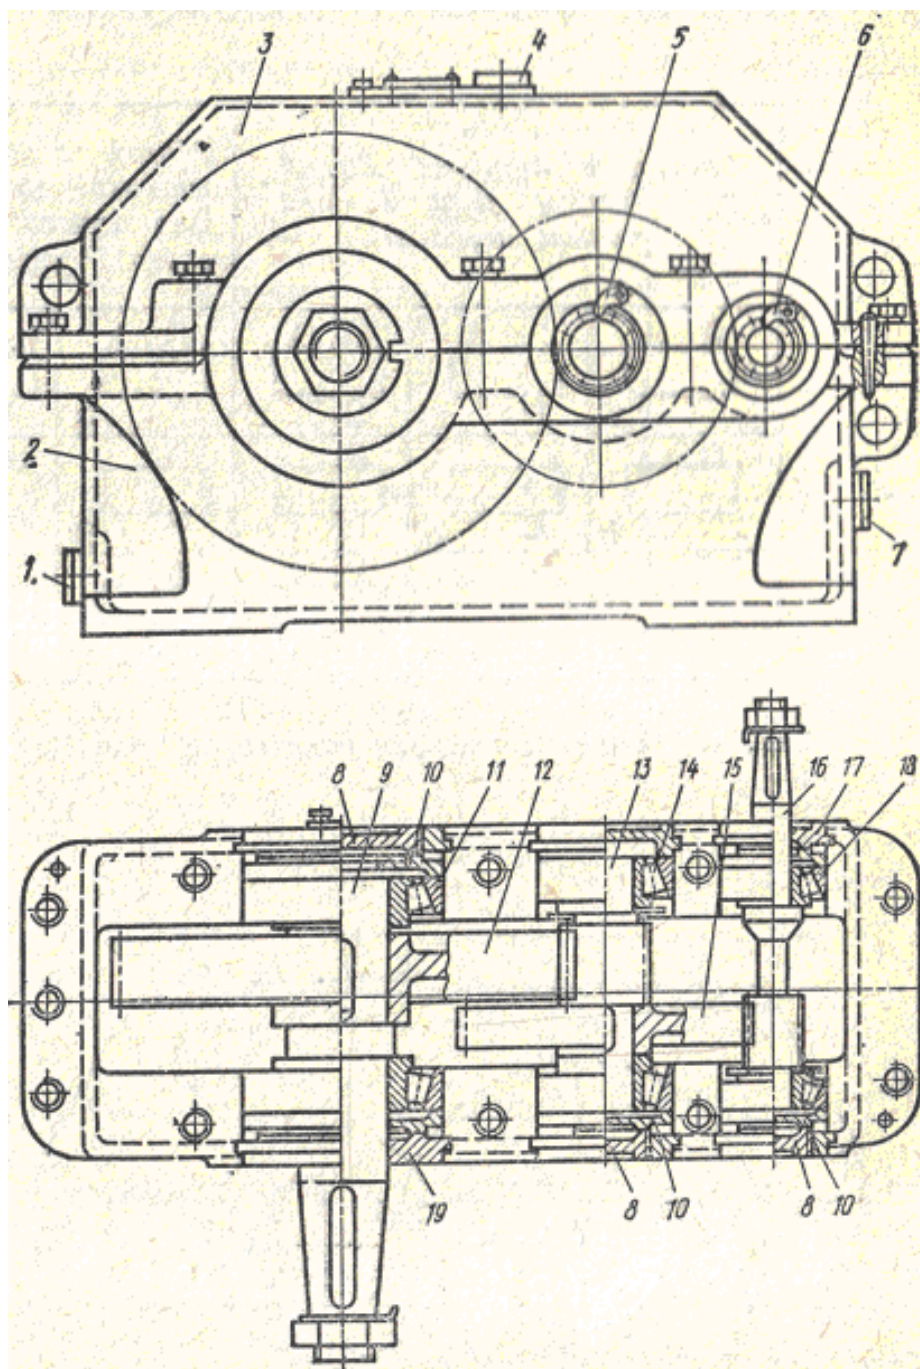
Общий вид цилиндрического двухступенчатого редуктора
